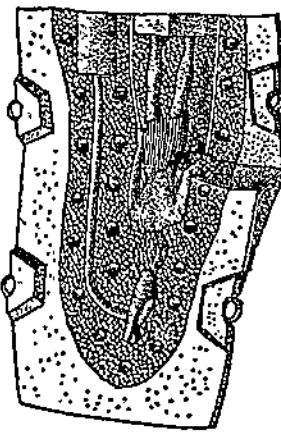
Отливка „под давлением“. Отливок в передней половинке формы.
